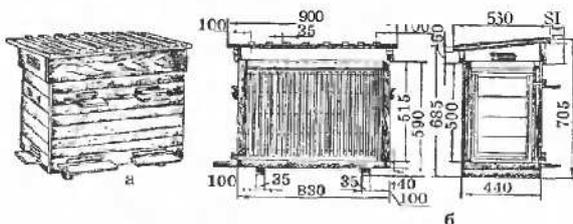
Украинский улей: а — общий вид; б — поперечный и продольный разрез
